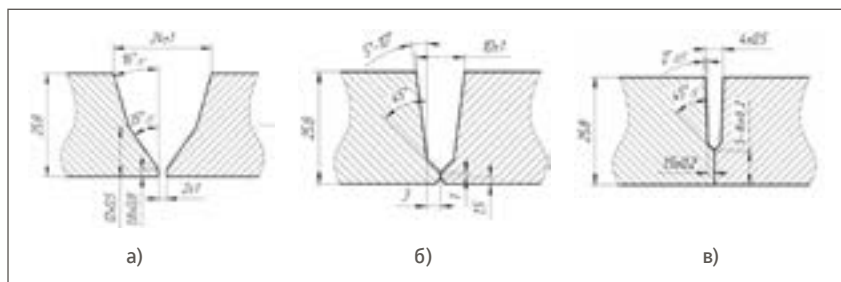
Разделки кромок: а) для ручной и механизированной сварки [5]; б) для сварки комплексом CRC-Evans [5]; в) для лазерной сварки
